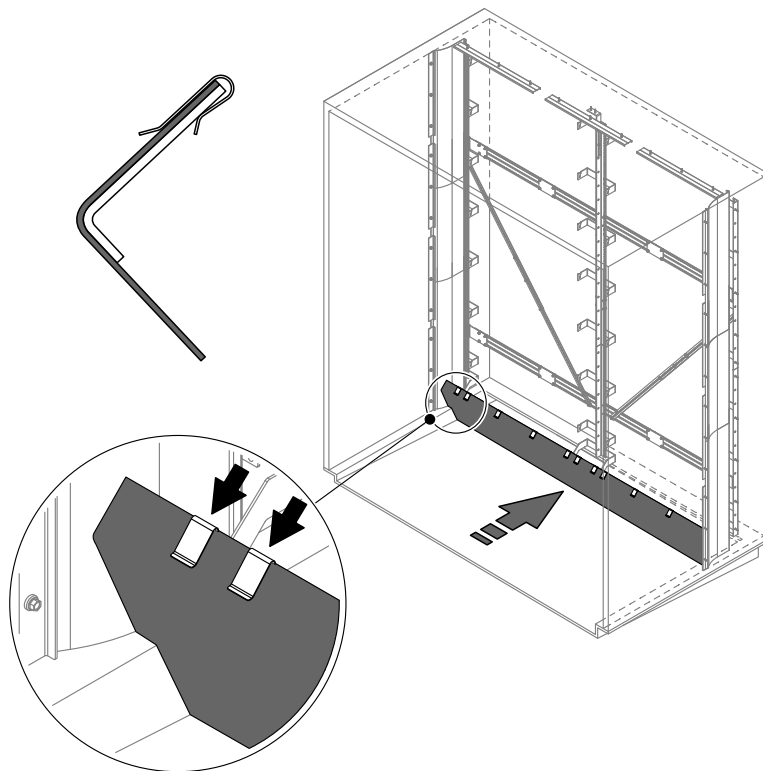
Montage du caoutchouc d'étanchéité du bac
